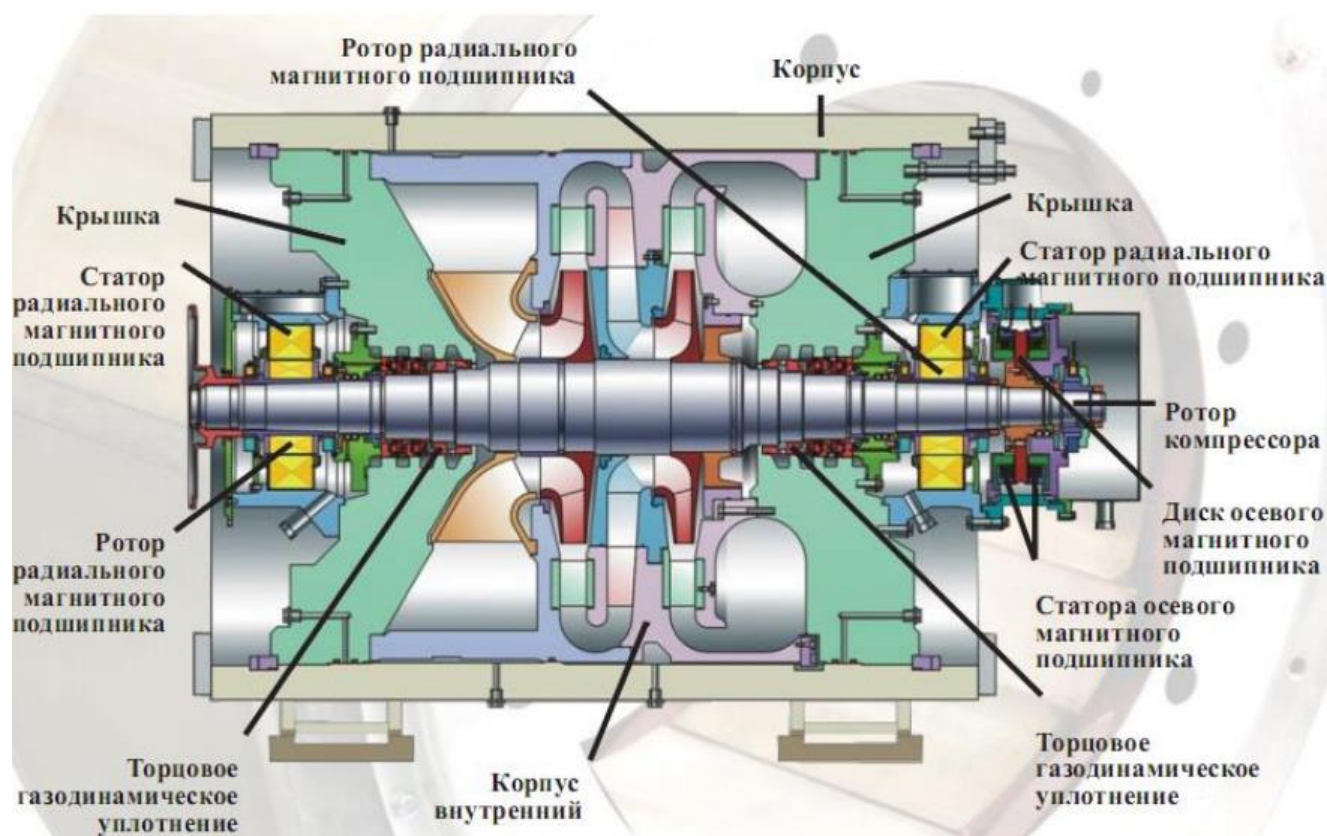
Устройство центробежного компрессора ГПА с ЭМП
